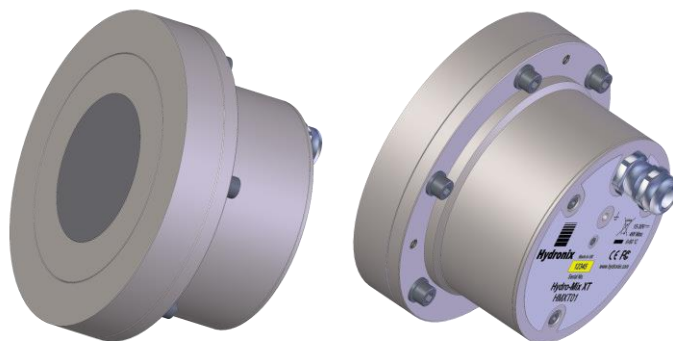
Piastra di fissaggio HMXT collegata al sensore Hydro-Mix XT
